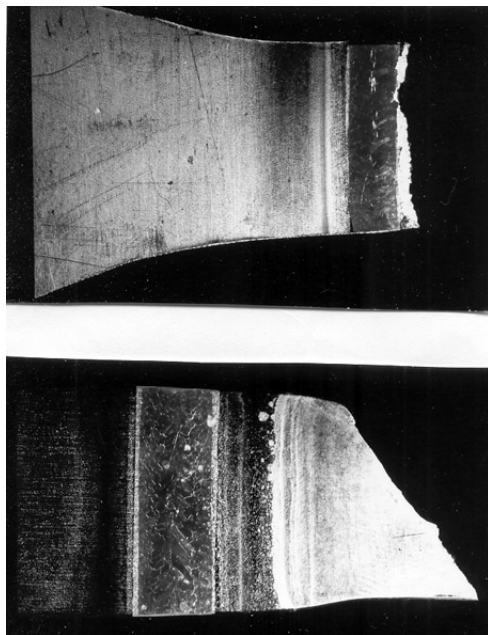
Характер разрушения сварных образцов при статическом растяжении
